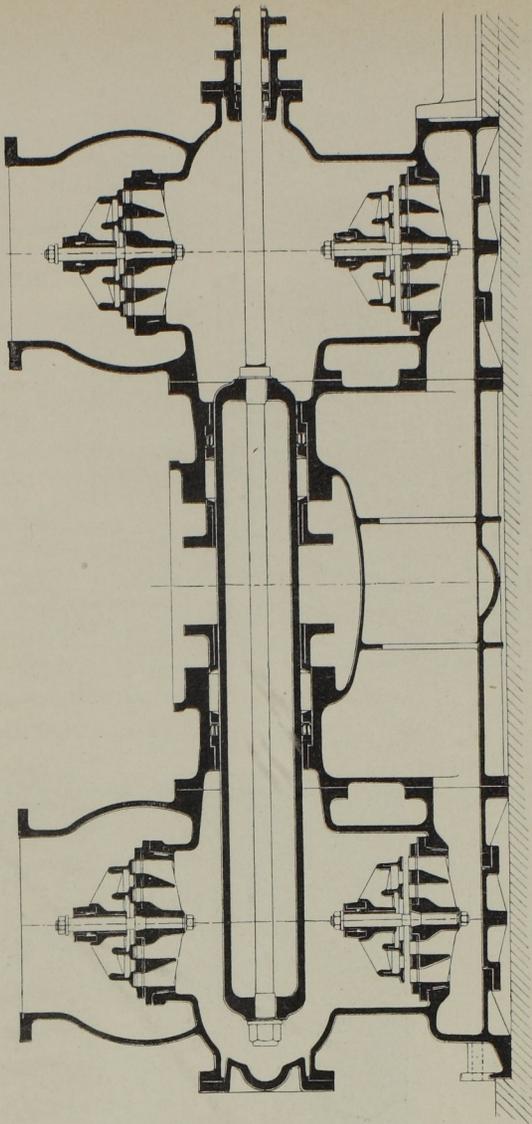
Längsschnitt der Pumpe für 8 cbm. Masst. 1 : 25.
